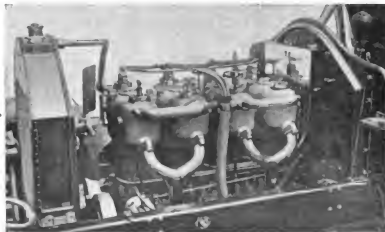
Motor der Beckmann-Automobile mit eigenartiger Kühlwasserführung.
